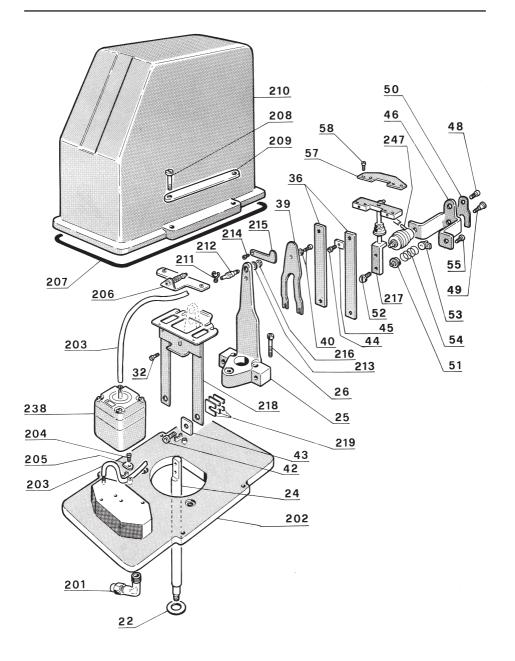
Vista esplosa dell'unità pneumatica di trasmissione. Exploded view of pneumatic transmission unit.
